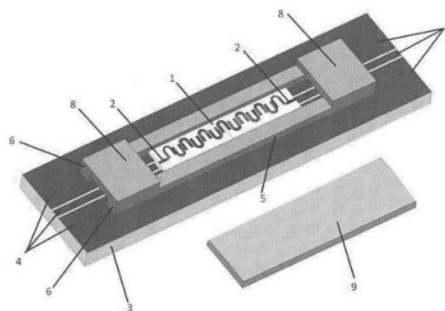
Схематическое изображение микрополоскового шпилечного фильтра под П-образной металлической крышкой на печатной плате
